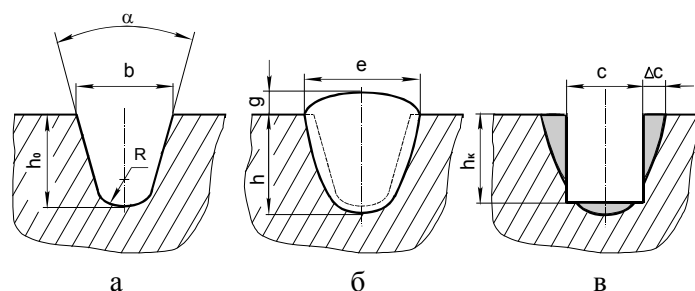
Профиль канавки под наплавку (а), вид наплавленного валика (б), профиль нарезанной канавки под компрессионное кольцо (в)
